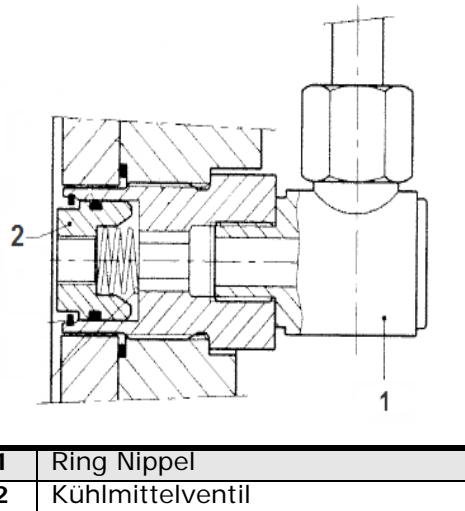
Live-Werkzeug TMM10i MDT20 Turret Kühlmittelventilanordnung
